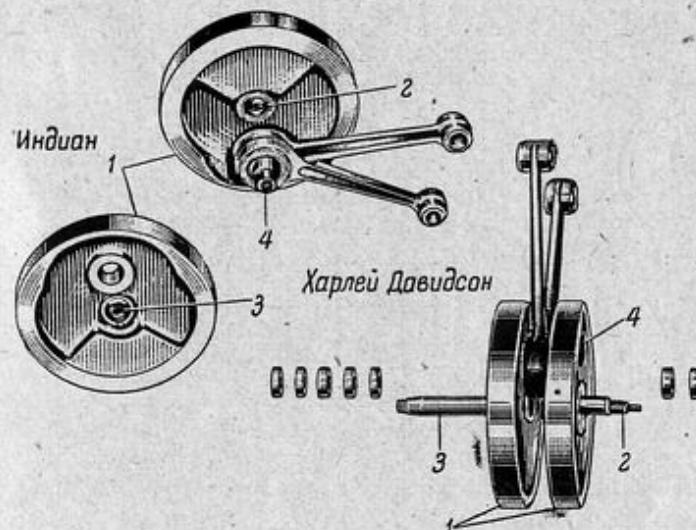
Разборные коленчатые валы двигателей Индиан и Харлей Дэвидсон:
